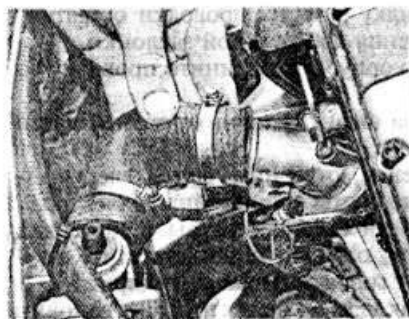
Отсоединение верхнего шланга радиатора от корпуса термостата — двигатель с двумя распредвалами
